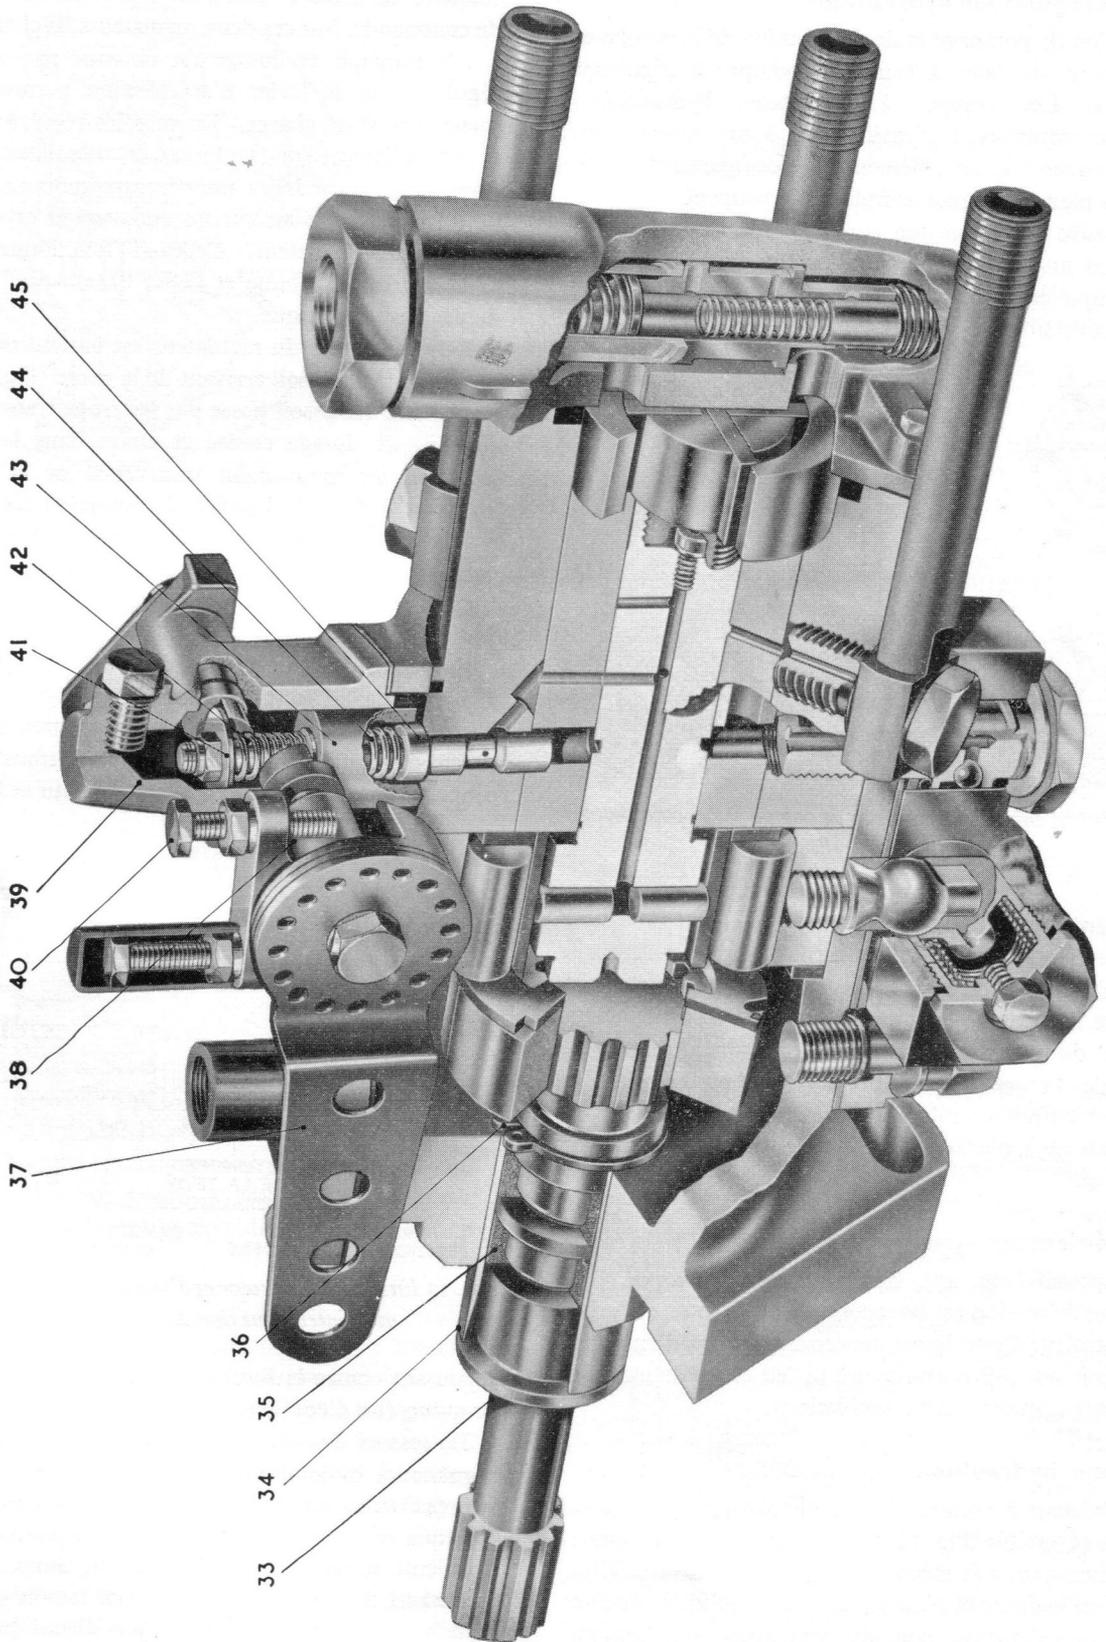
Pompe à régulateur hydraulique à montage réversible équipée d'un dispositif d'avance
